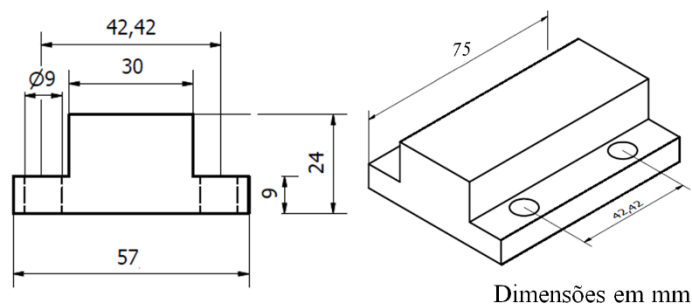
Geometria e dimensões do corpo de prova para o fresamento
